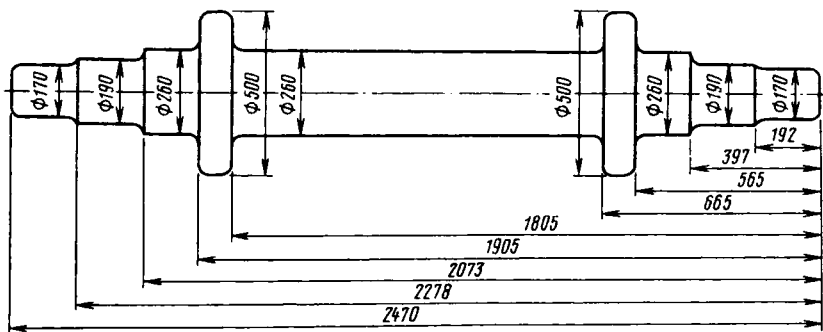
Главный приводной вал эскалатора Н-40 очереди III и IV
